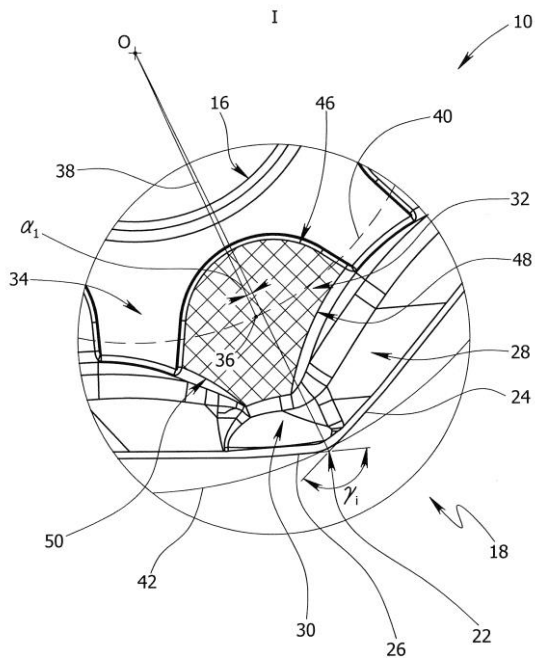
Увеличенный фрагмент I вида сверху на первую поверхность для отвода стружки многогранной двухсторонней режущей пластины
